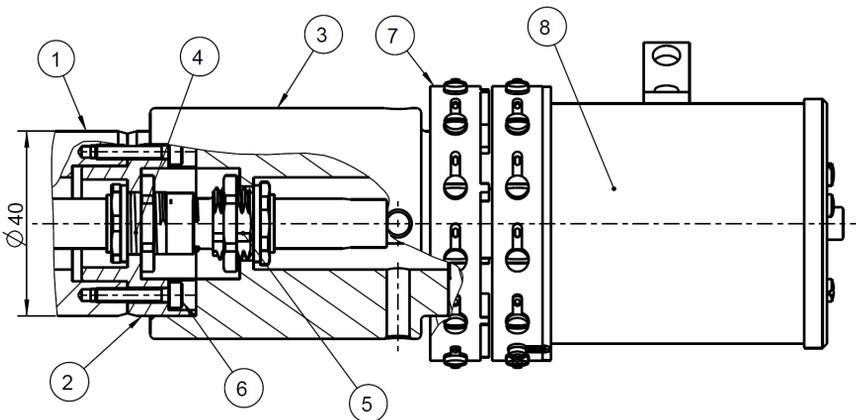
Kupplungssystem: 1 = Wellenende der Getriebewelle; 2 = Buchsenzapfen; 3 = Adapterrohr; 4 = Buchse; 5 = Stecker; 6 = Befestigungsschraube; 7 = Rotorbaugruppe; 8 = Statorbaugruppe
